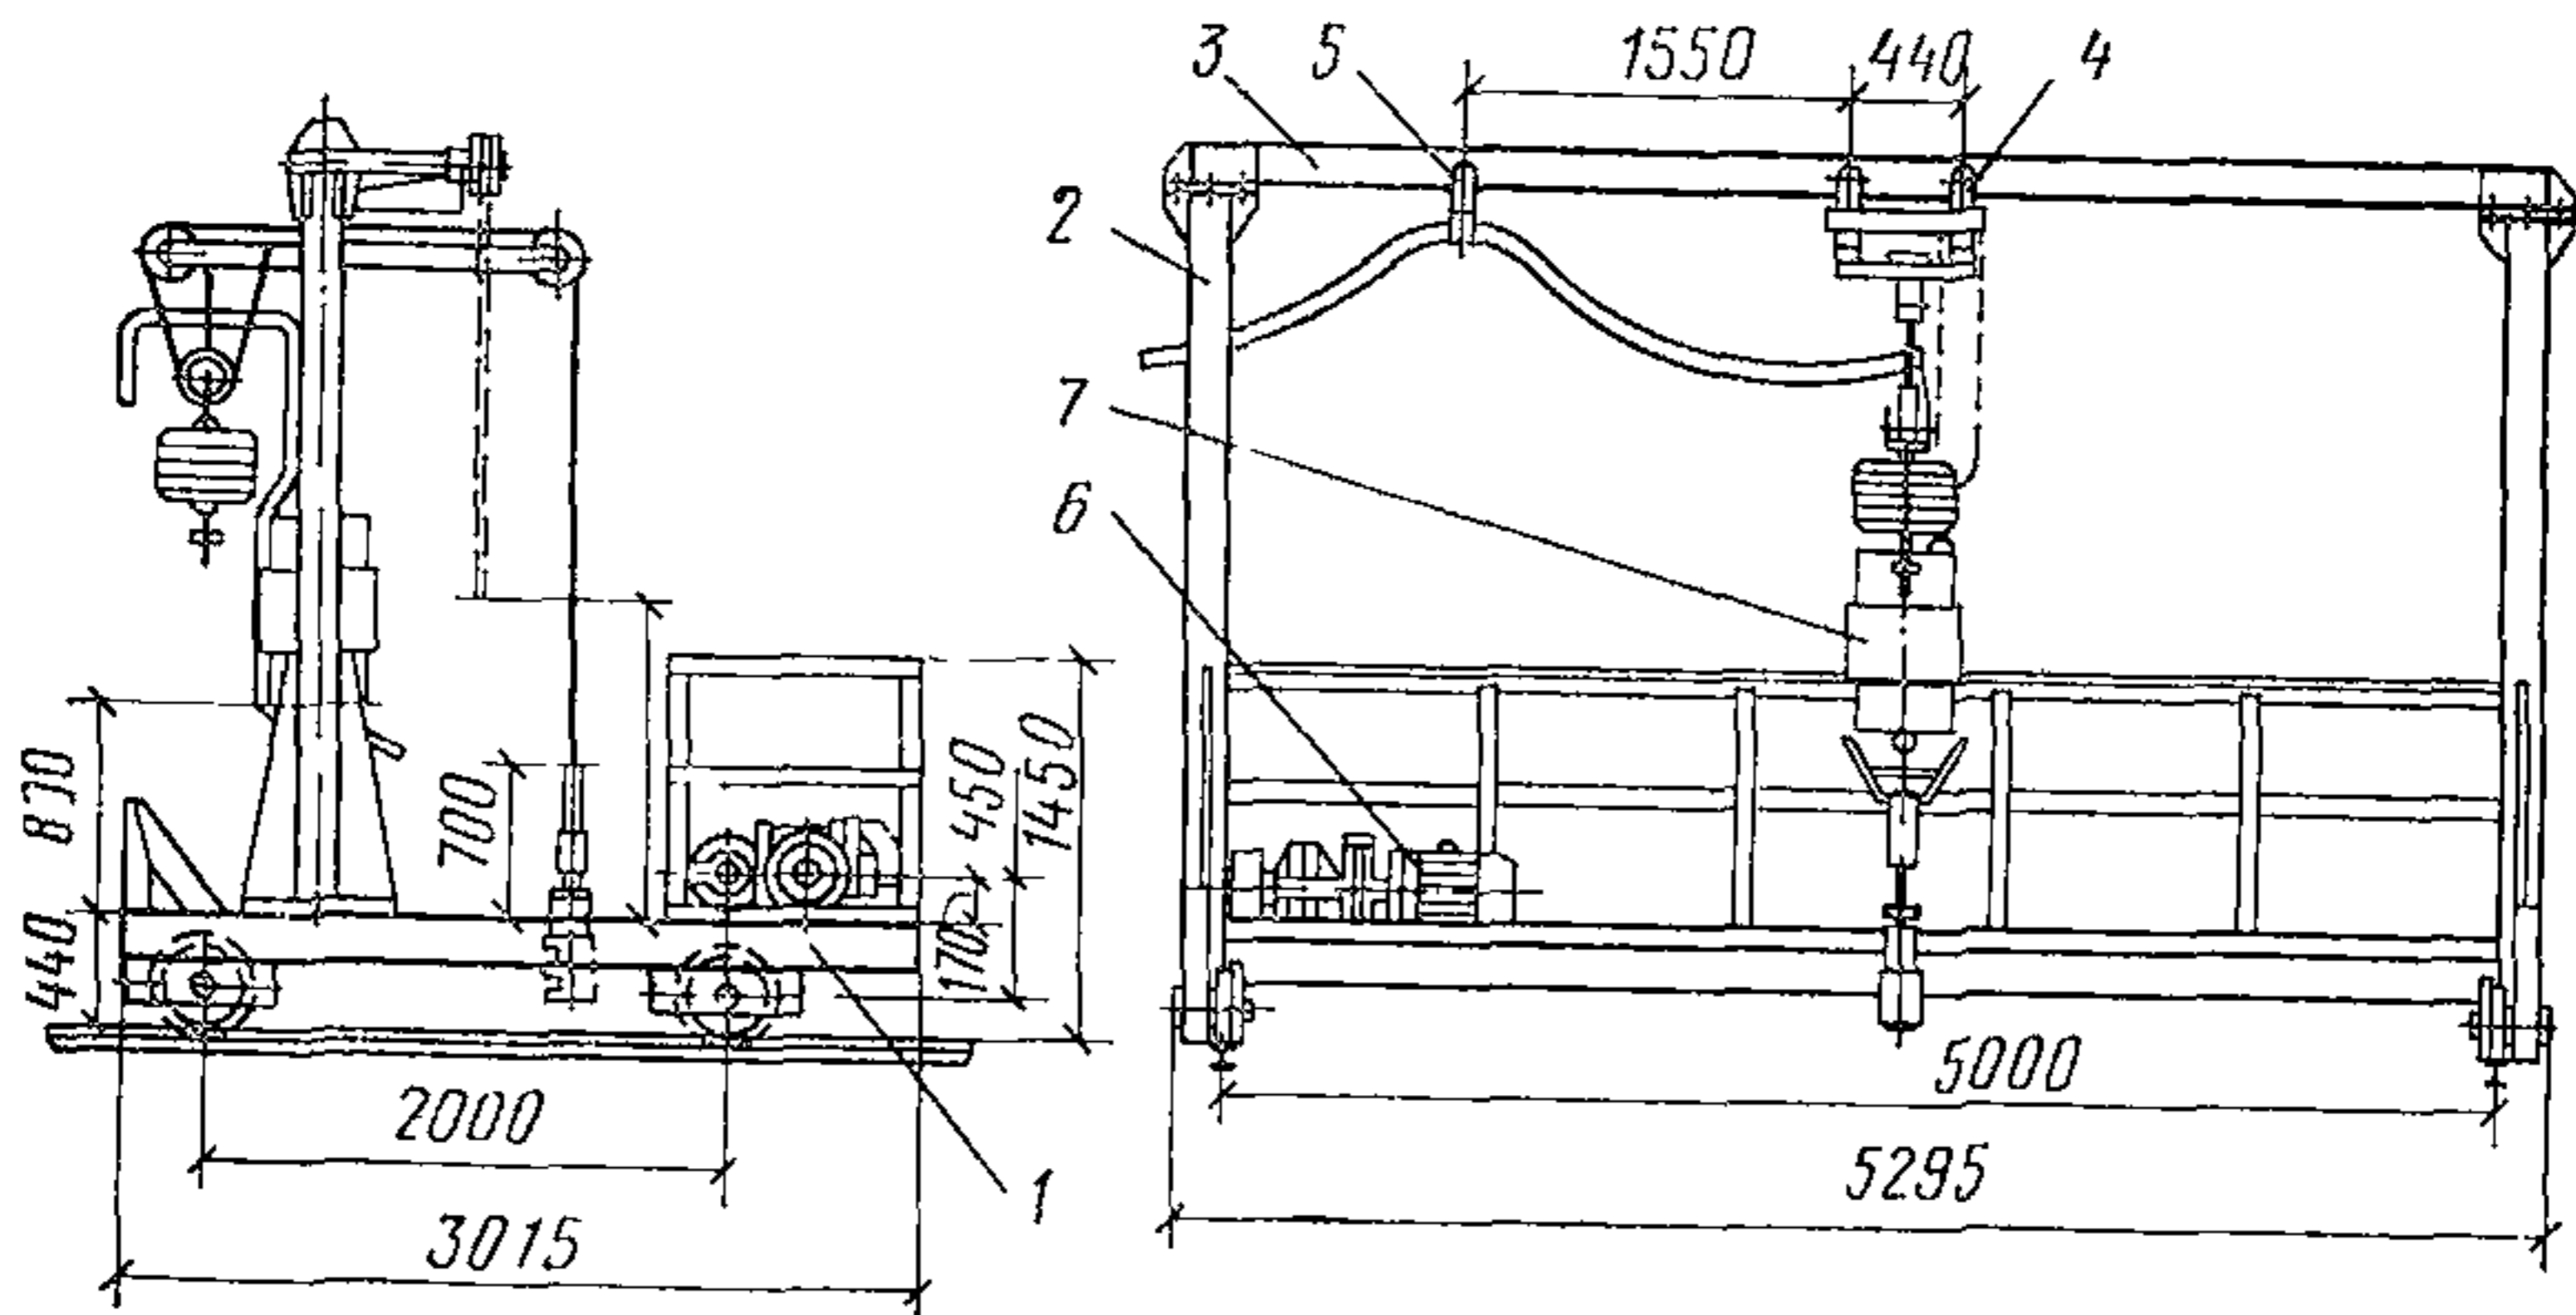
Самоходное устройство для подвески сварочных клещей
